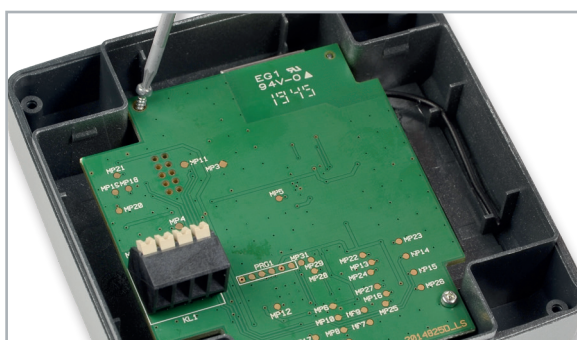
Das endgültige Fixieren der Platine im Gehäuse erfolgt mit zwei Schrauben.
